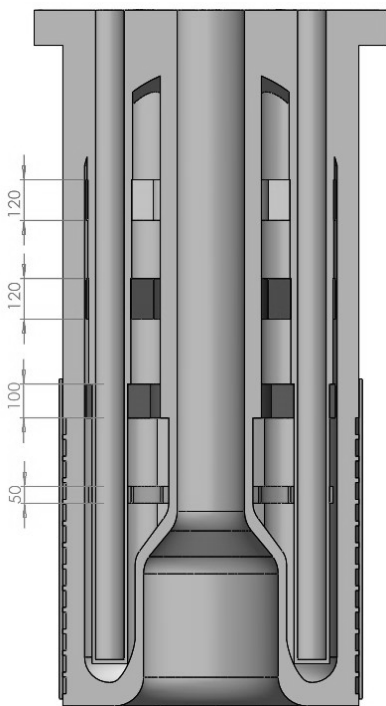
Конструктивная схема оптимизированного корпуса АЗ ИЯР ВИР-3
